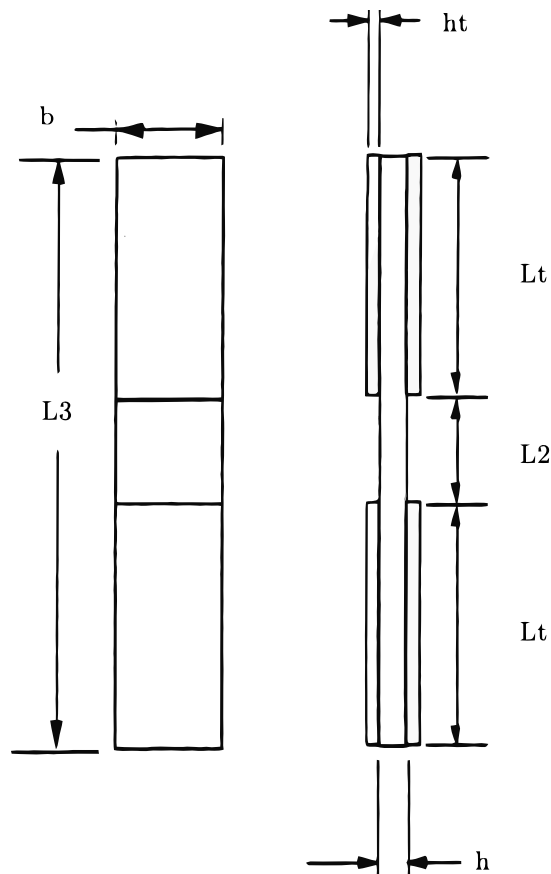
Geometrie der Druckproben gemäß ASTM D3410
